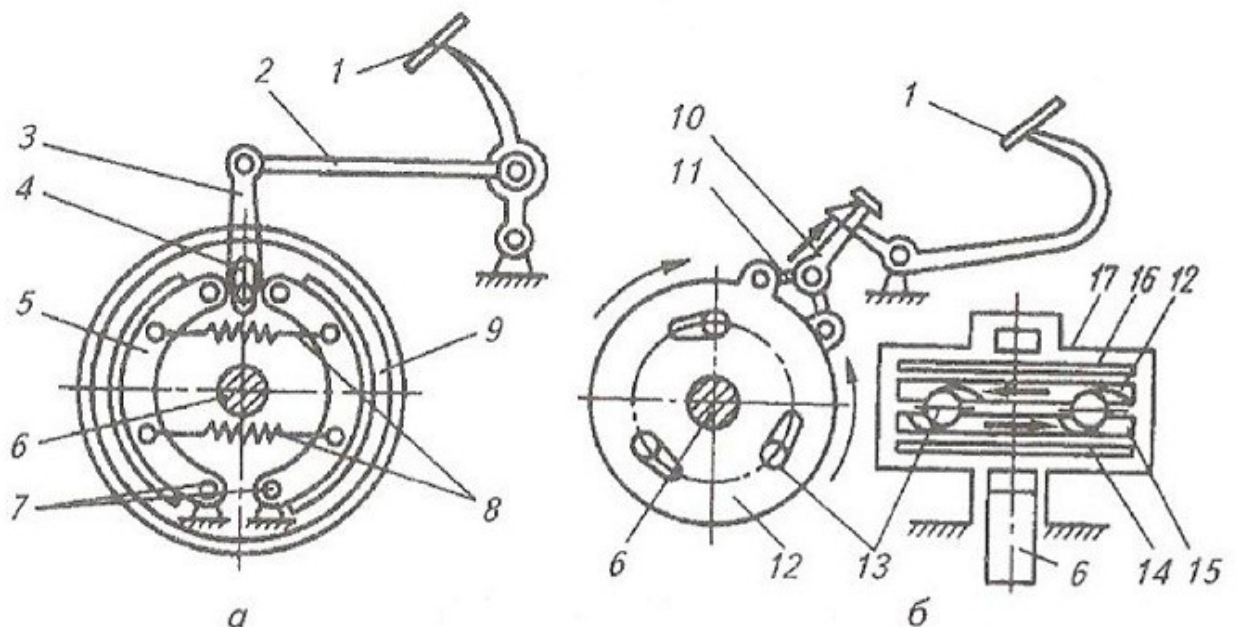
Схемы колесных тормозов: а - колодочного; б - дискового; 1 - педаль; 2 - тяга; 3 - рычаг; 4 - разжимной кулачок; 5 - колодка; б - затормаживаемый вал; 7 - оси поворота колодок; 8 - стяжные пружины; 9 - тормозной шкив; 10 - тяга с регулировочной гайкой; 11 - серьга; 12, 15 - нажимные диски; 13 - шарик; 14, 16 - диски с фрикционными накладками; 17 - картер
